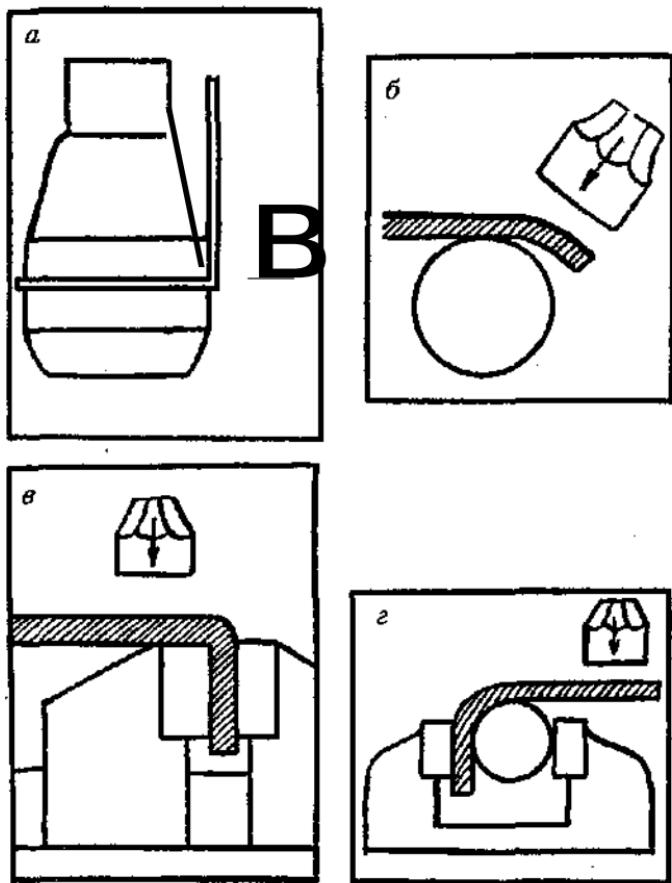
Гибка металлического листа в горячем состоянии: а — тонкой заготовки; б — толстой заготовки; в — гибка по радиусу по рогу наковальни; г — то же, по оправке, зажатой в тиски.
